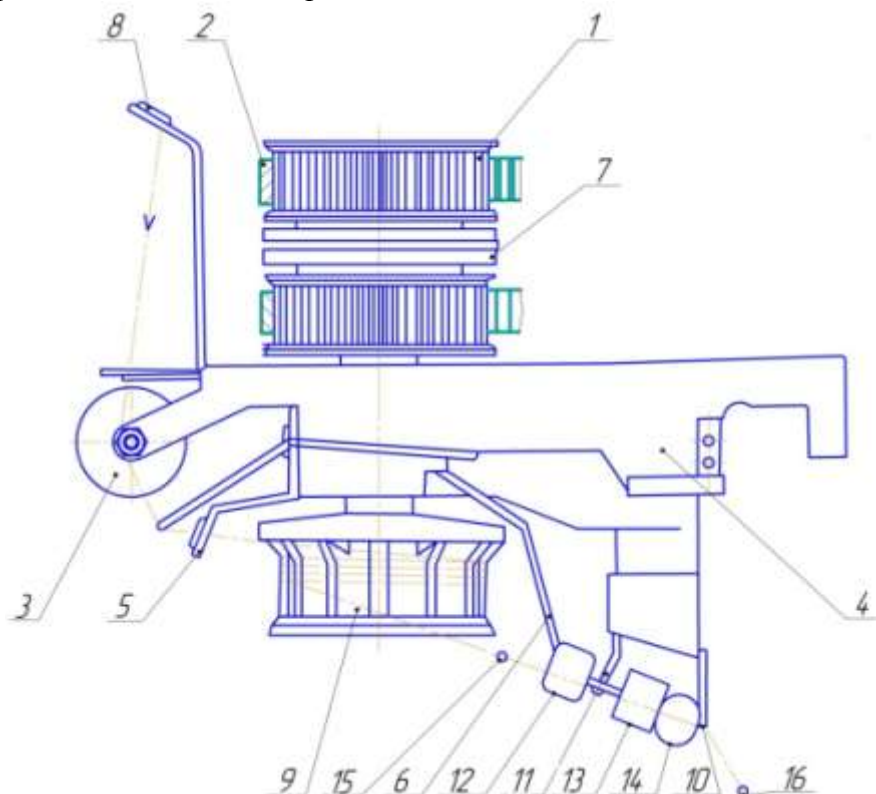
Модернизированная конструкция механизма нитеподачи
